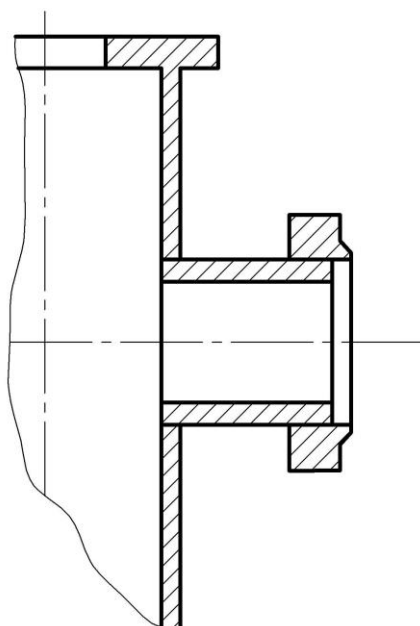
Изображение неразъемного соединения деталей сваркой.
